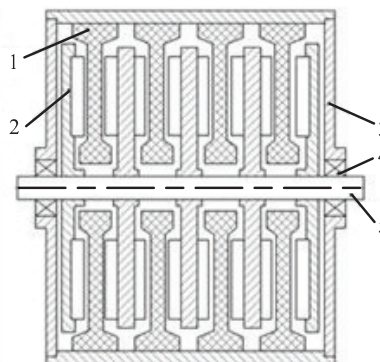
Модульная дисковая машина: 1 – обмотка статора; 2 – роторный узел; 3 – корпус; 4 – подшипники; 5 – вал
